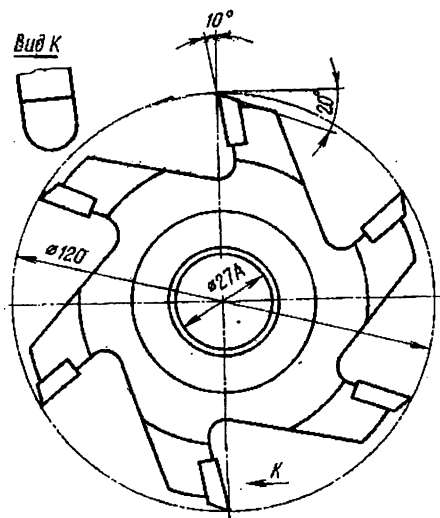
Фреза насадная с пластинками из твердого сплава
